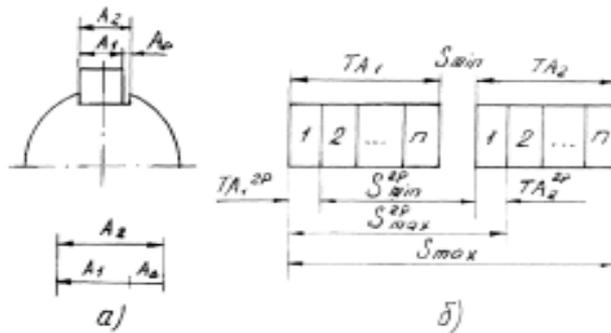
Схема для выборочной сборки «шпоночный паз - шпонка»
